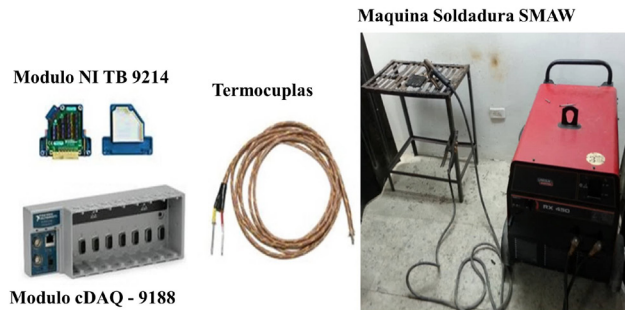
Módulos NI para adquisición de datos. Sensor de temperatura: termopares. Máquina soldadura SMAW
